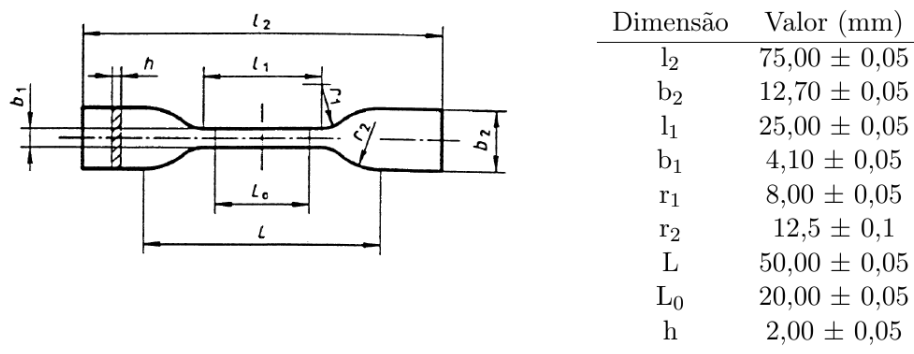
Desenho técnico do provete usado e suas dimensões [70].
